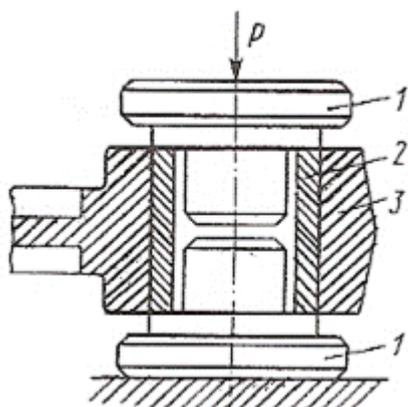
Приспособление для осаживания втулок: 1 — пуансоны; 2 — втулка; 3 — головка шатуна
